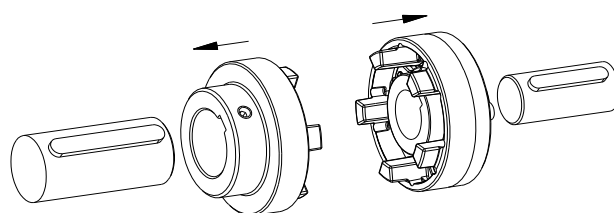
Montage von Nabe und Flanschnabe mit Nockenring
